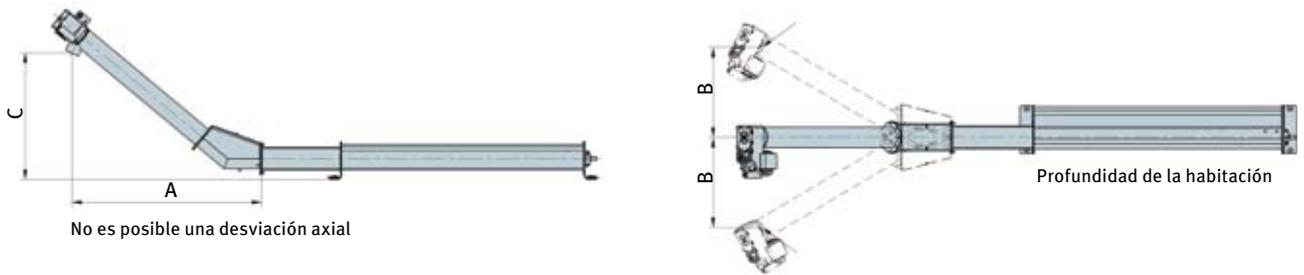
Disposiciones posibles del tornillo sinfín en codo
